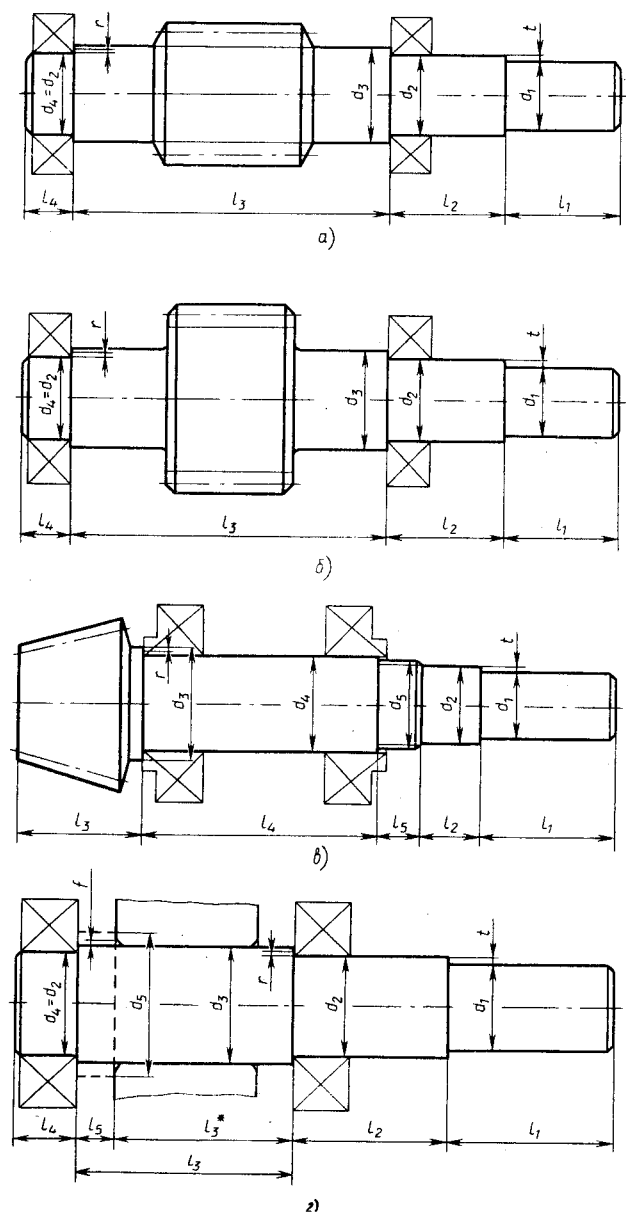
Типовые конструкции валов одноступенчатых редукторов:
